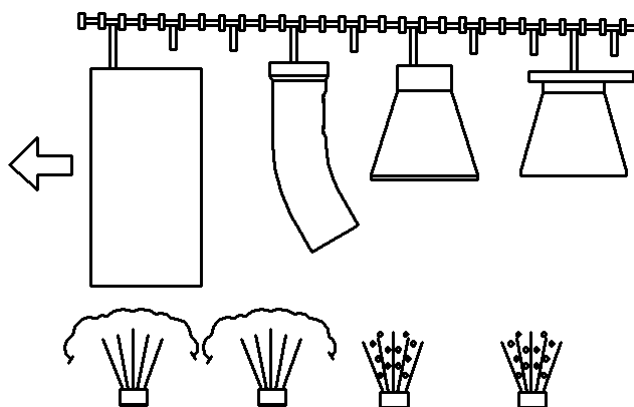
Подготовка деталей к сварке
